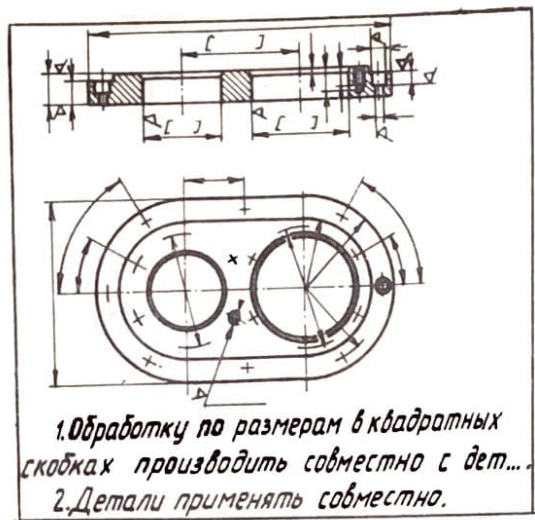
Нанесение размеров на деталях, обрабатываемых совместно
